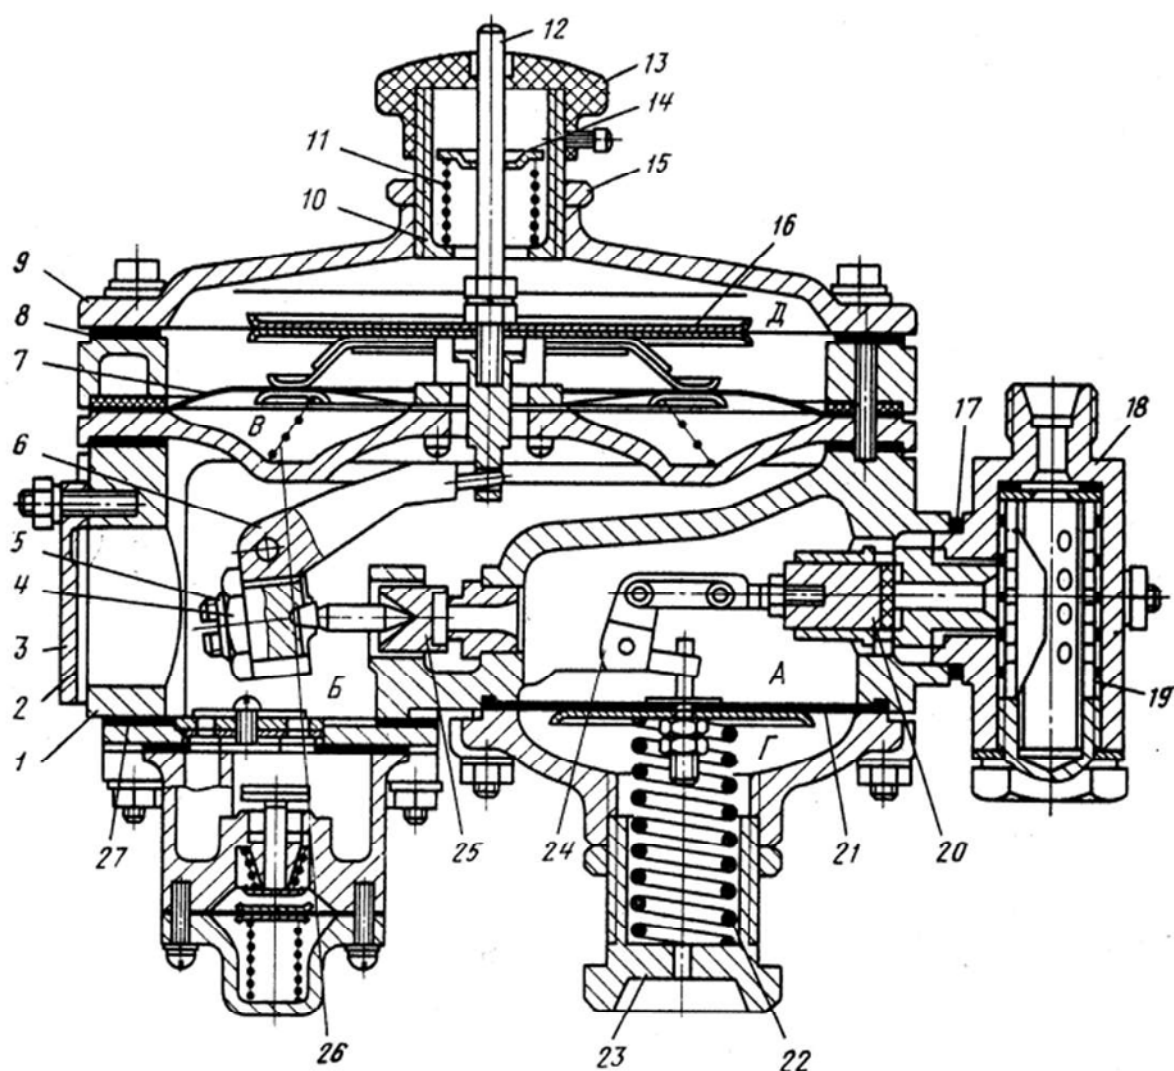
Газовый редуктор низкого давления: А - полость первой ступени; Б - полость второй ступени; В - полость разгрузочного устройства; Г и Д - полости атмосферного давления; 1 - корпус газового редуктора; 2 - прокладка; 3 - крышка; 4 - контргайка регулировочного винта; 5 - регулировочный винт клапана низкого
